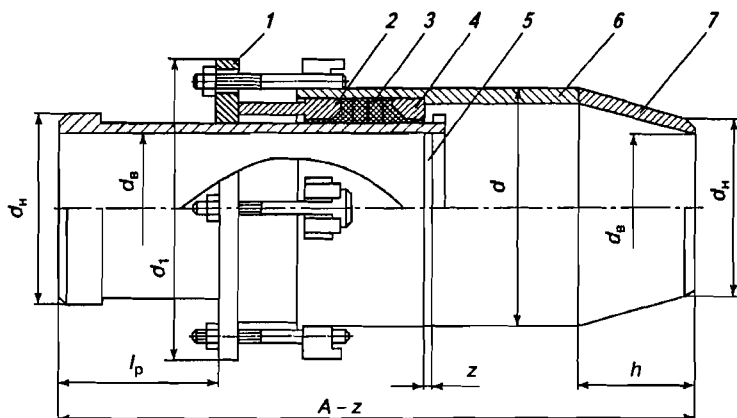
Односторонний сварной сальниковый компенсатор
